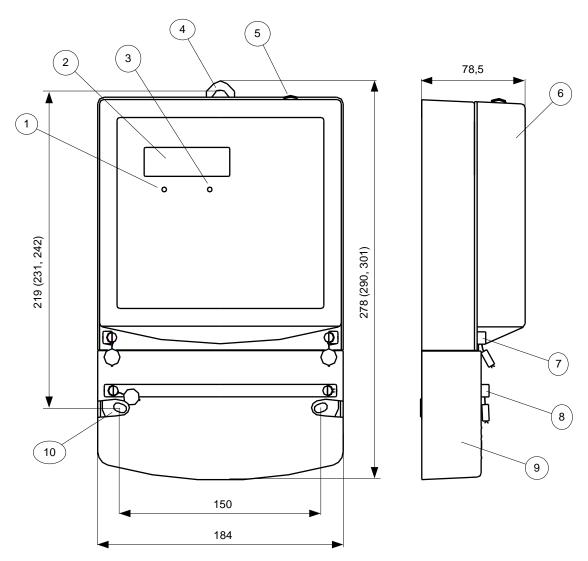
Внешний вид, габаритные размеры и места установки пломб на корпусе типа 4
